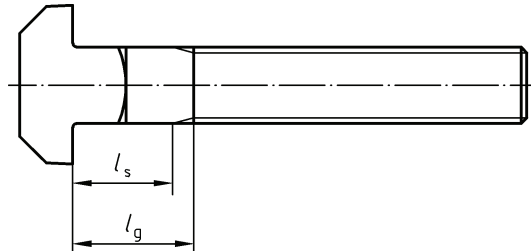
Hammerschraube, Form B mit langem Gewinde
